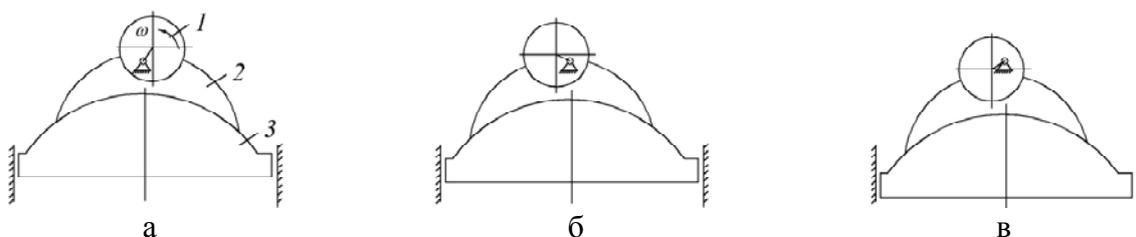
Схема кривошипно-ползунного КШМ с группой Ассура второго вида: а – положение I; б – положение II; в – положение III
